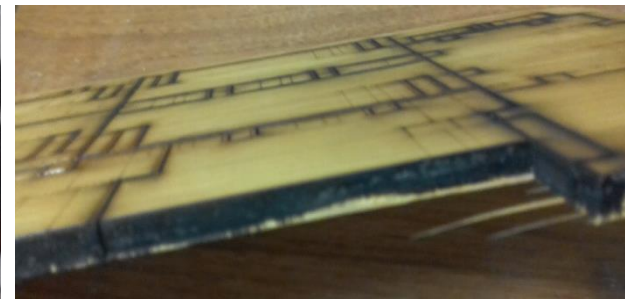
Retirada das peças: fendilhamento da placa de bambu laminado. Fonte: Autora (2018).
